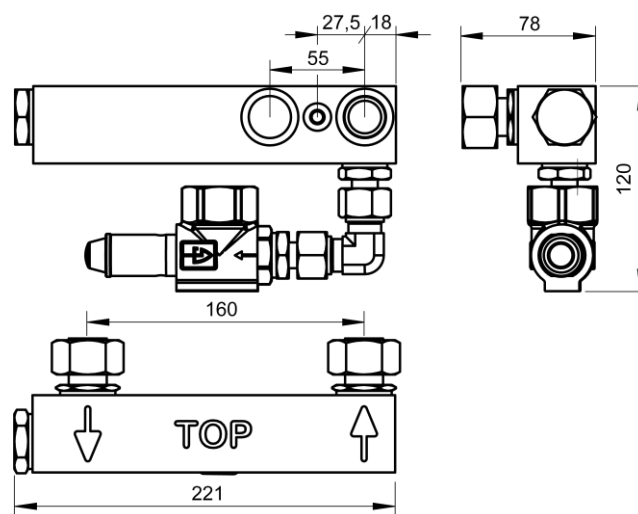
Dimensiuni HB-200/230 adaptor pentru HB-TP180-12
